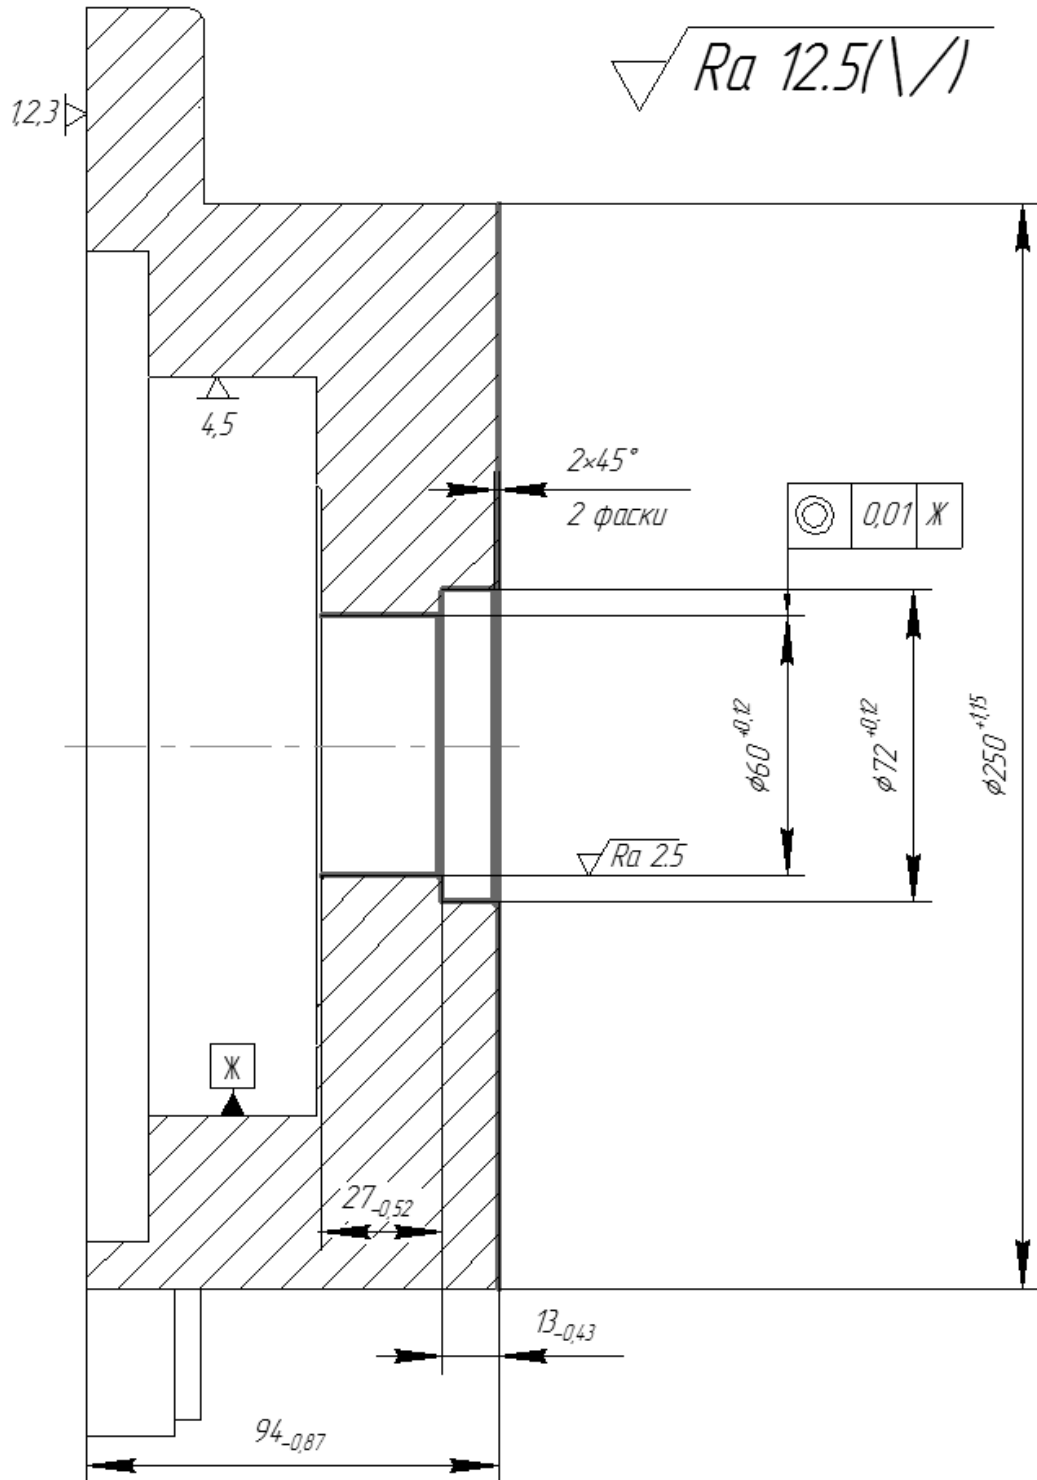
Ескіз обробки заготовки на операції 025
